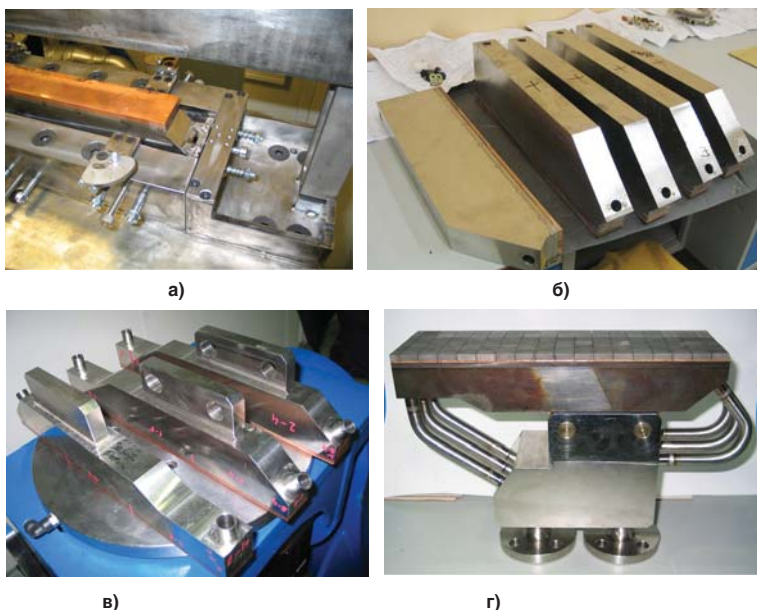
Корпуса элементов мишени ЦСД после сборки и постановки прихваток (а), после лазерной сварки (б) и после механической обработки и радиографического контроля (в) и в сборке мишени под гидравлические испытания (г).
